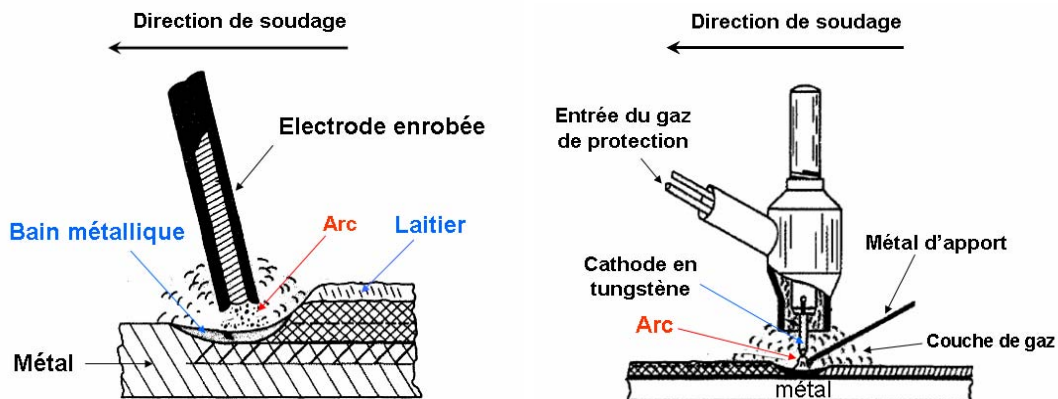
a) Soudure MMA . b) Soudure TIG.
